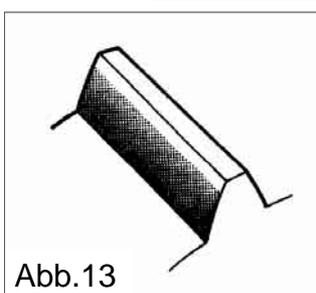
Das Tellerrad befindet sich zu nah am Triebbling und arbeitet auf Fußfläche des Zahns. Die Ringmutter B von Abb. 6 ist loszuschrauben, um dann die Ringmutter A im gleichen Ausmaß anzuziehen.
